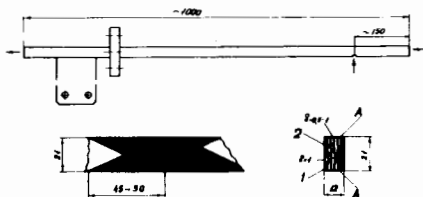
Токоввод на 3 кА: 1 - пластина, 2 - оплетка, А - место сварки.
